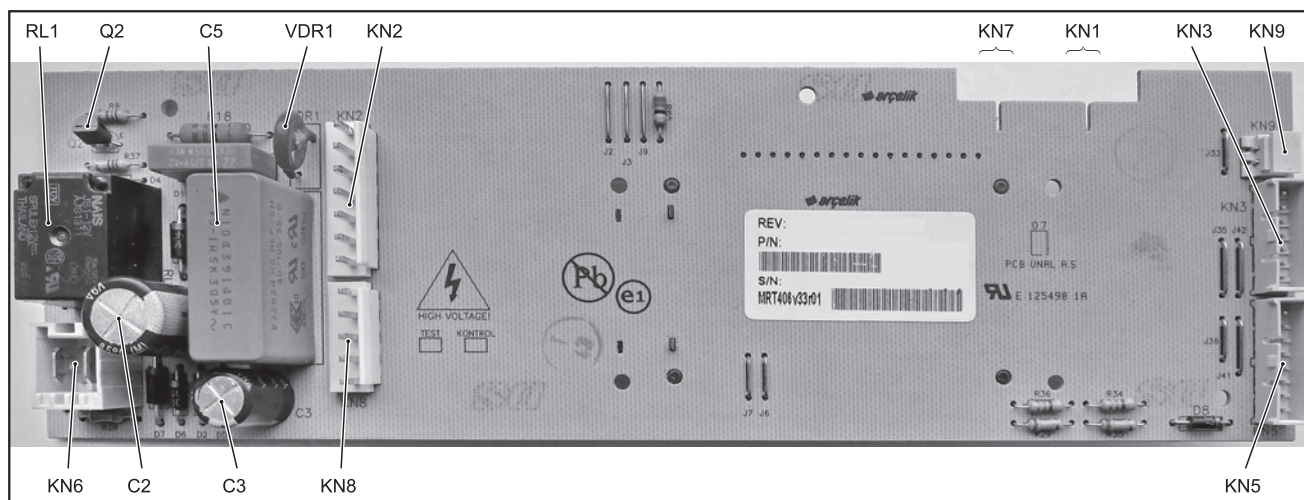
Внешний вид ЭМ, его основные компоненты и соединители (вид сверху)
